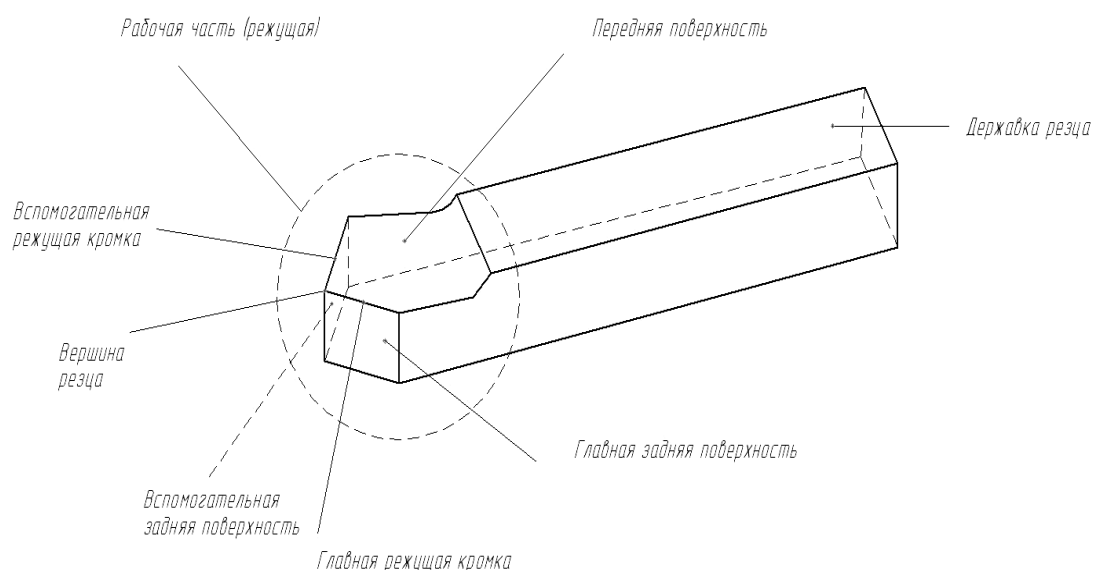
Рабочие поверхности и режущие кромки резца
